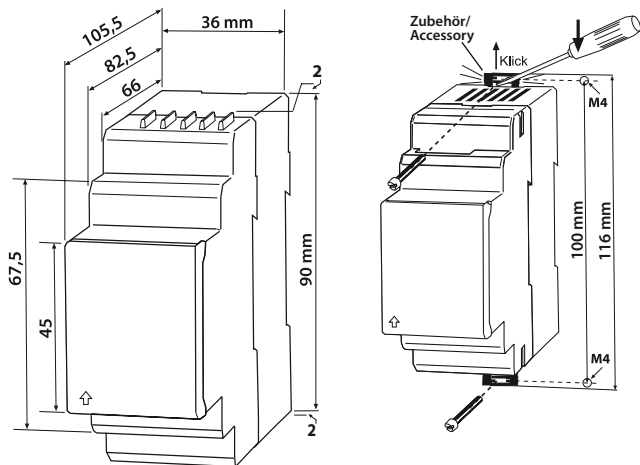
Maßbild, Skizze für Schraubbefestigung
